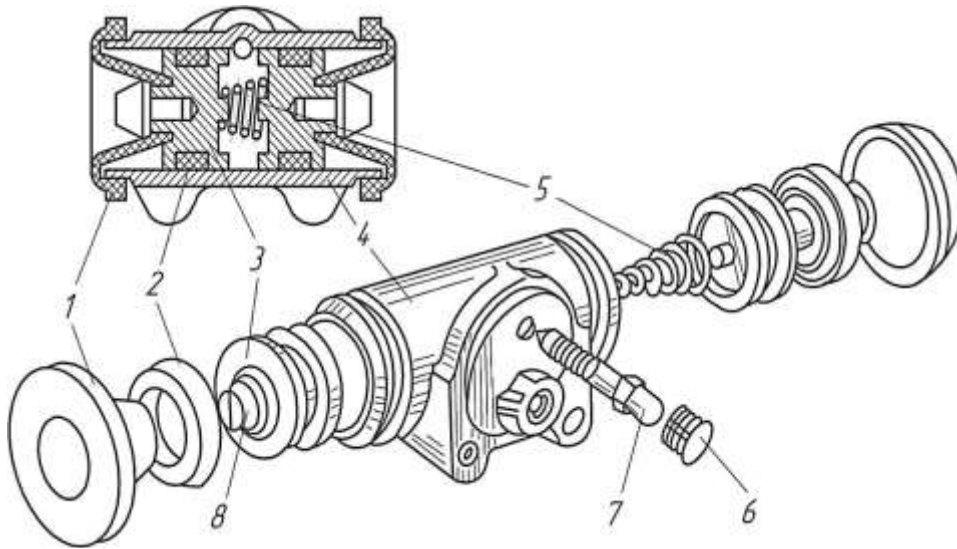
Колісний поршневий гідроциліндр гальм:
